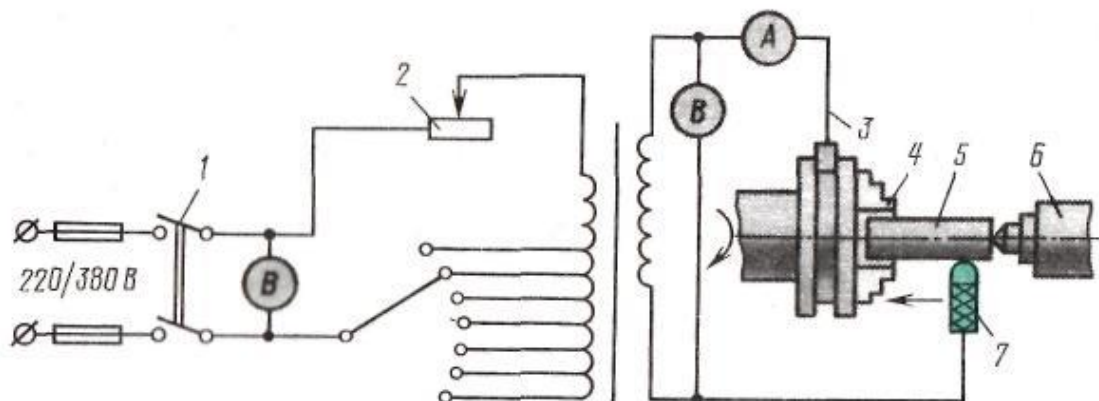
Схема восстановления размера вала электромеханической обработкой: 1 — рубильник; 2 — реостат; 3 — провод вторичной обмотки; 4 — патрон станка; 5 — деталь; 6 — задняя бабка станка; 7 — инструмент.
